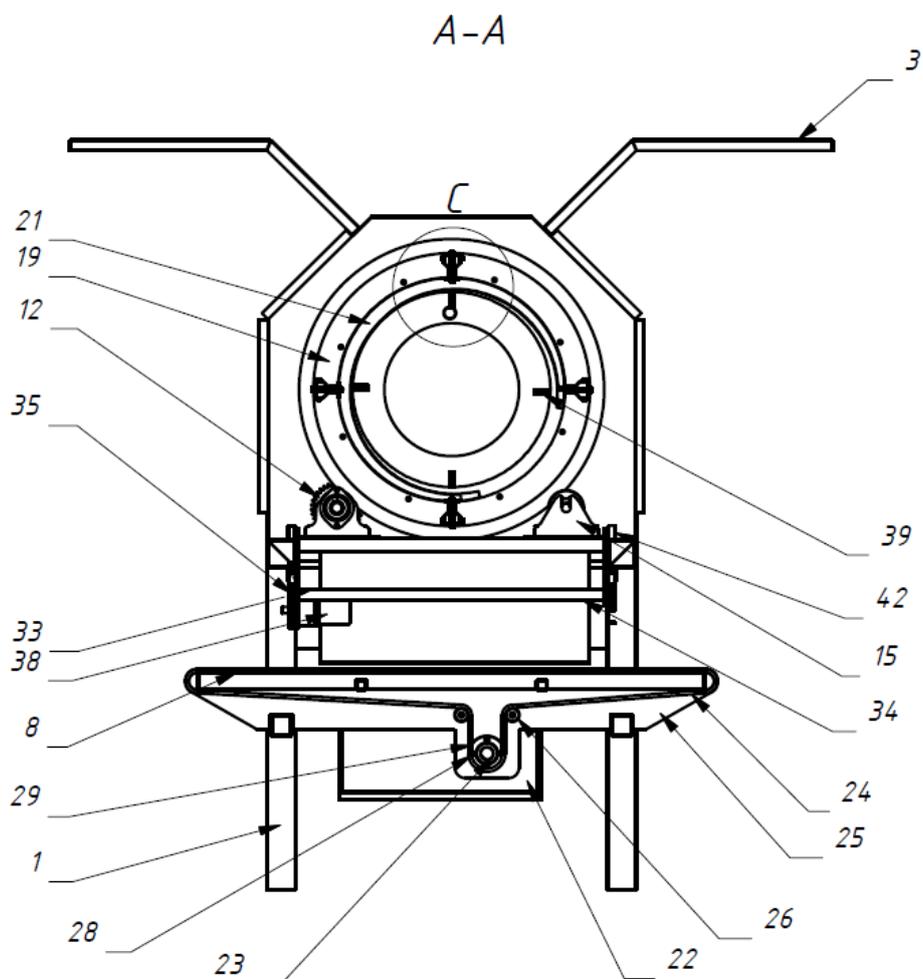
Схема машины для сортировки рыбы, вид спереди
